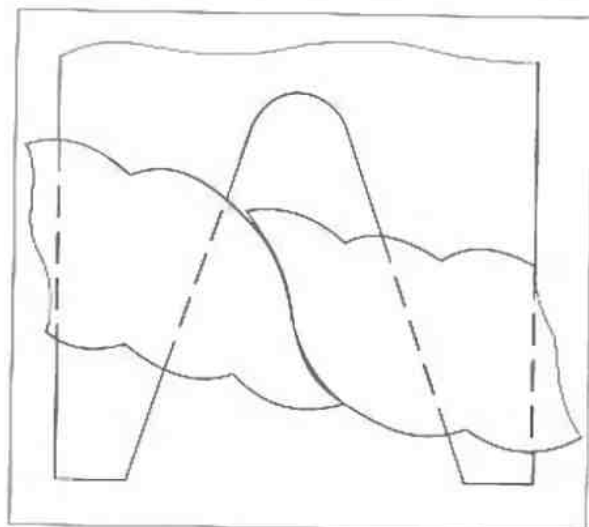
Доска с вырезом (приспособление для подгонки стыков деталей)
